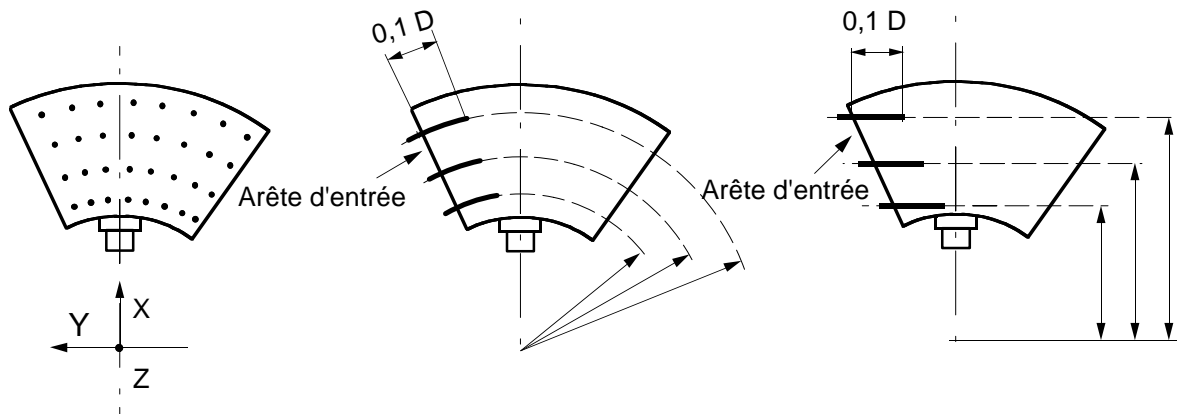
Roue de machine axiale. Exemple de positions des sections ou des points de mesure du profil des aubes
